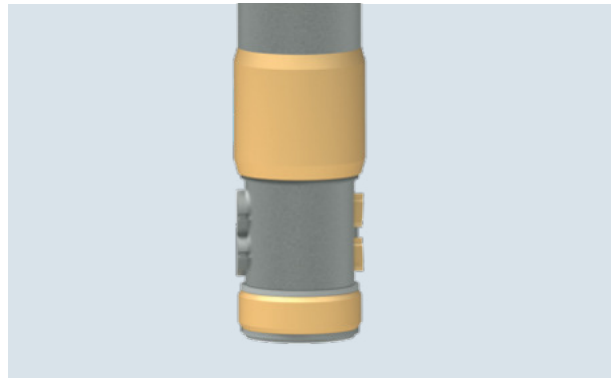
SOLO mit eingefahrenem Messer, welches durch eine Führungsbüchse vor und hinter dem Messer geschützt wird.
